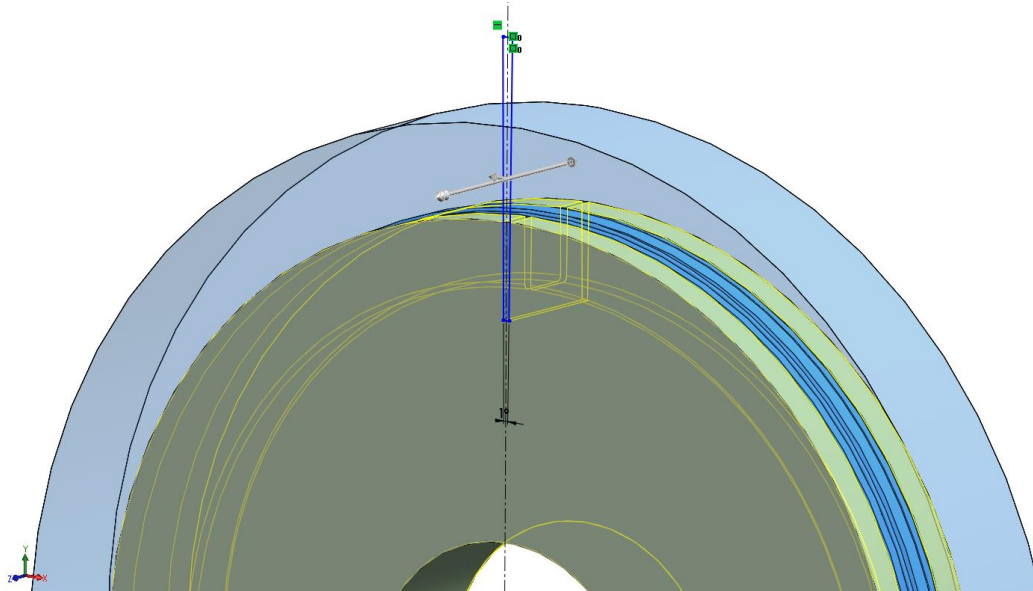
Στεγανωτικό S9B55 – SKF , O-ring από NBR ,slide ring από PTFE.
